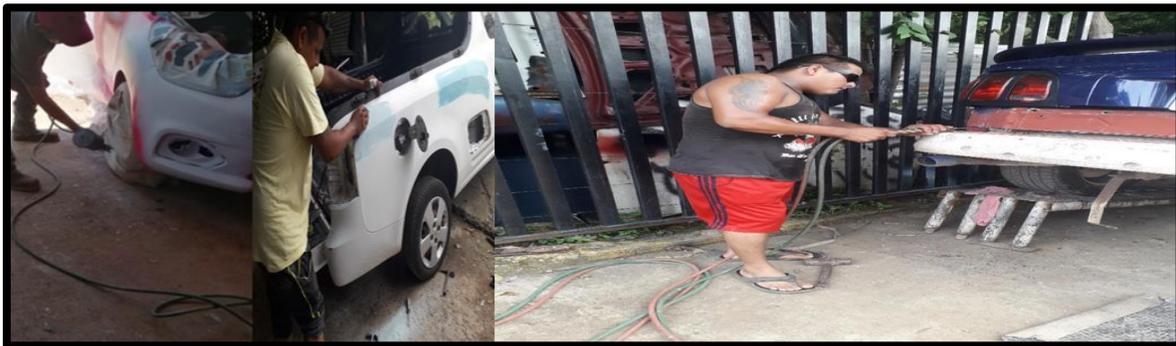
Aplicación de pintura, lijado y soldadura
